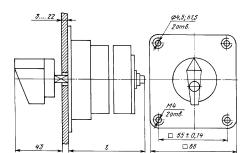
Габаритные, установочные размеры и масса переключателей типа ПКУЗ 11:
